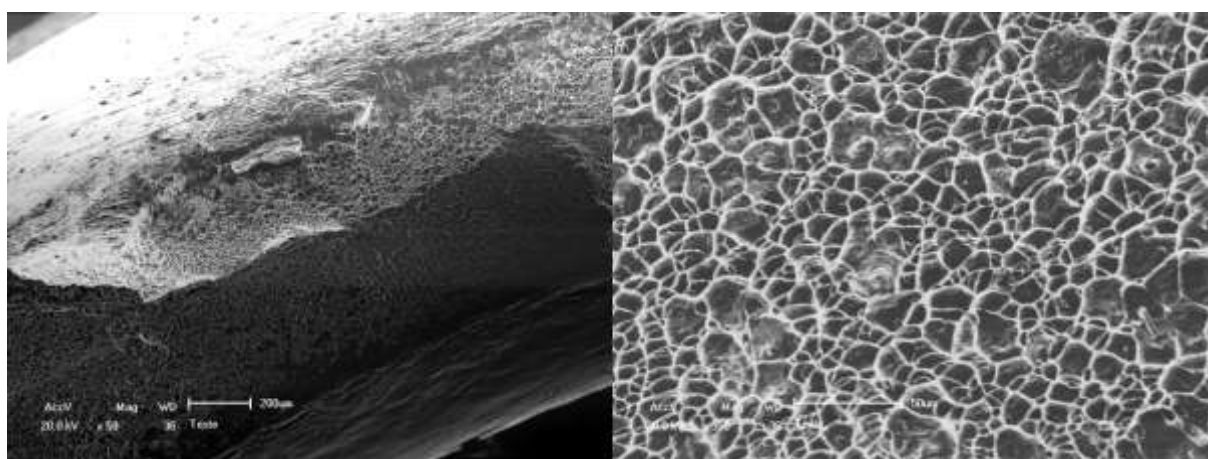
Superfície de fratura do CP - SI_027_09_39 (região apresentando modo de fratura dúctil representado pelos “dimples”).
